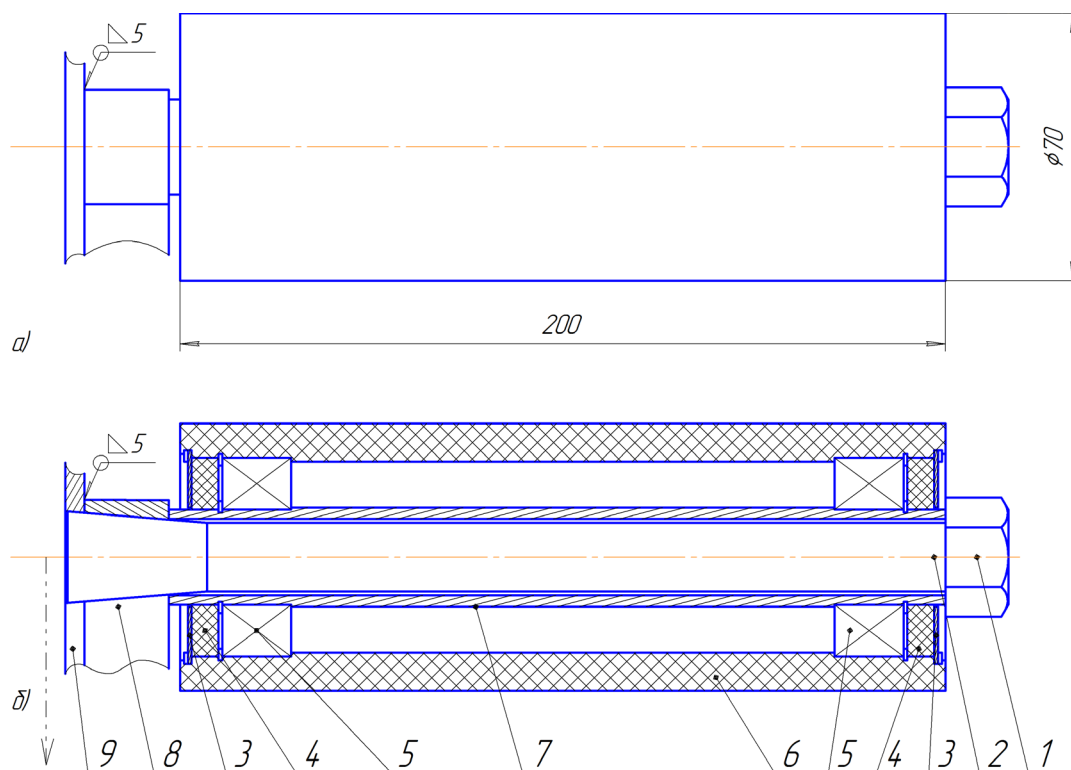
Опорный каток: а – вид; б – сечение совместно с гусеницей: 1 – гайка; 2 – ось; 3 – защитная шайба; 4 – уплотнение; 5 – закрытый подшипник; 6 – обод; 7 – втулка; 8 – планка; 9 – корпус ковша
